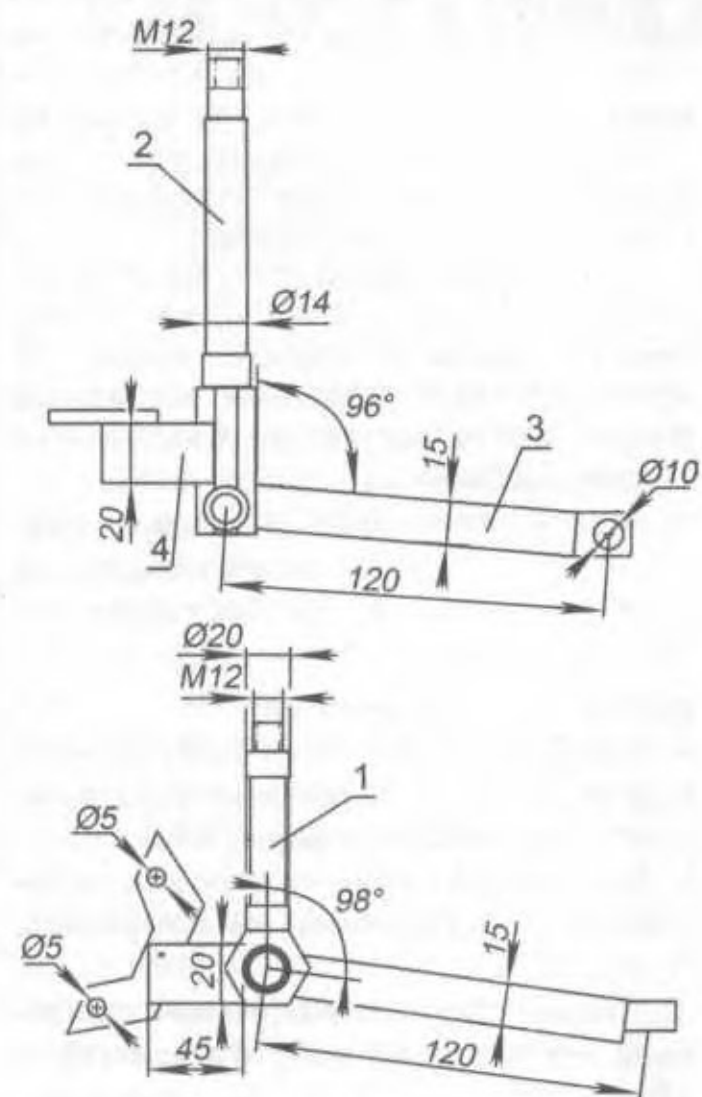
Поворотный кулак (правый, левый – зеркально отображенный): 1 – цапфа колеса; 2 – шкворень; 3 – поворотный рычаг; 4 – кронштейн тормозного механизма (калипера)
